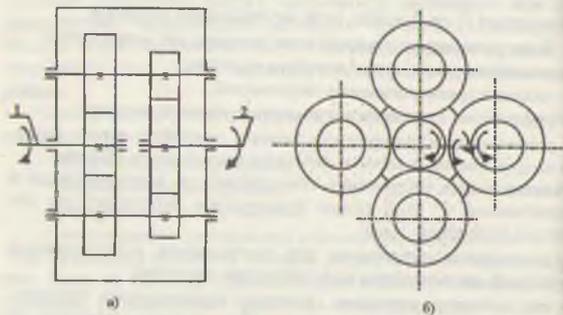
Четырехдорожечный редуктор Баварской фирмы BHS: а) разрезка редуктора; б) свертка редуктора
